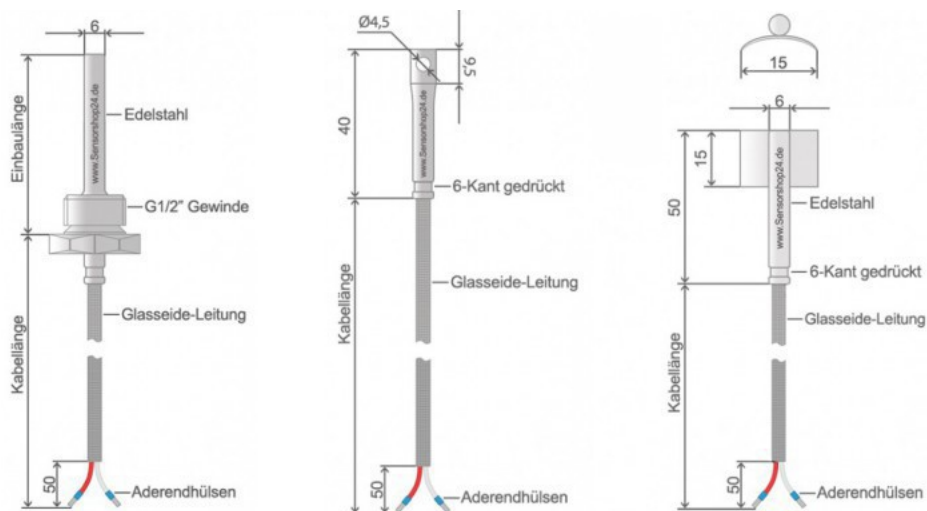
Einschraubsensor (links), Oberflächensensor (mittig), Rohranlegefühler (rechts) [15]
